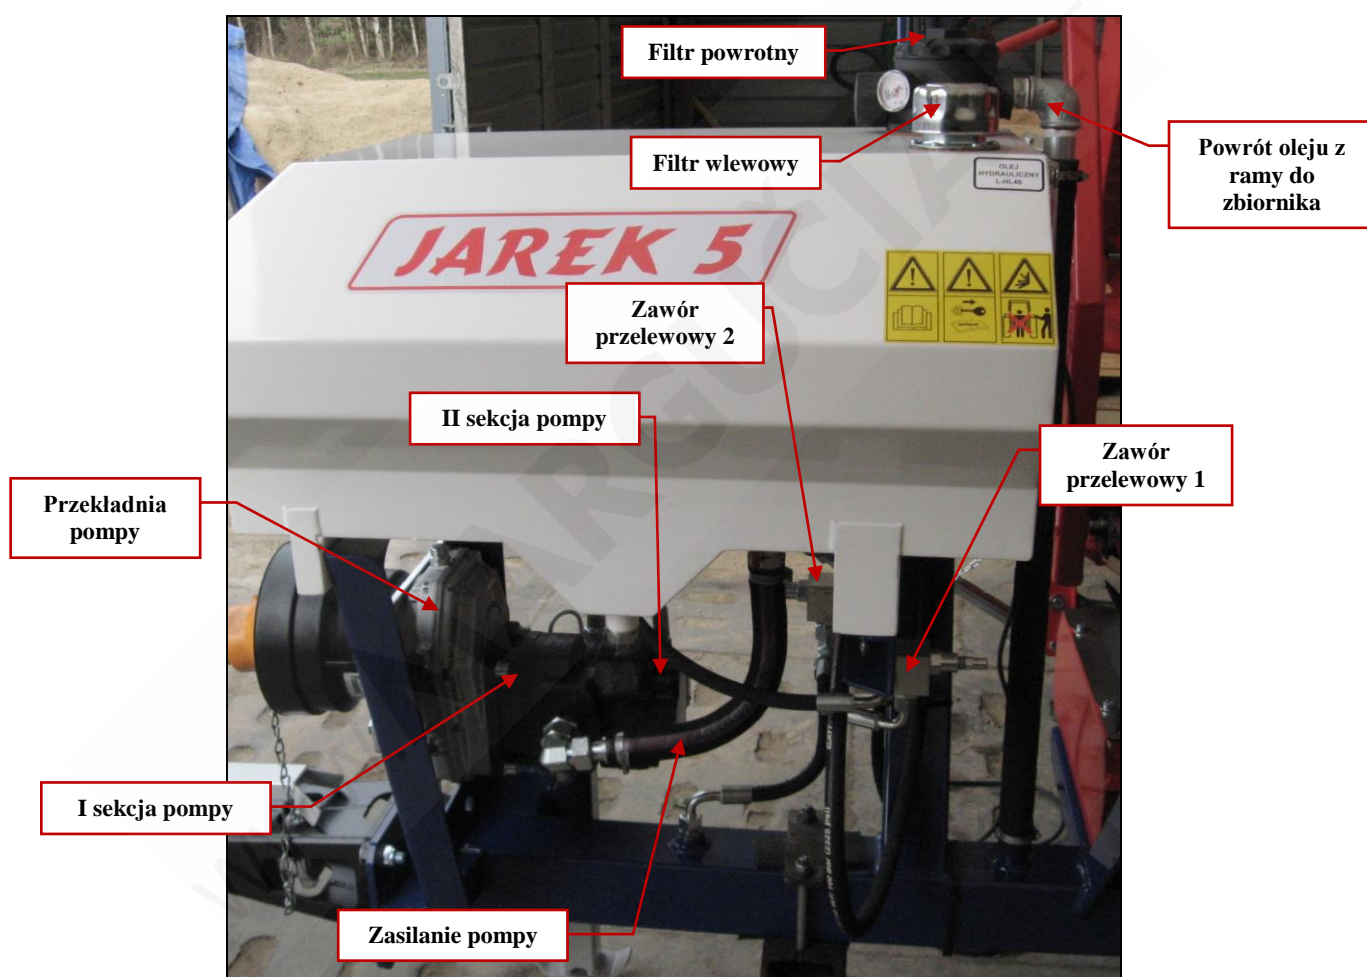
Elementy układu hydraulicznego – przekładnia, pompa, zawory przelewowe
